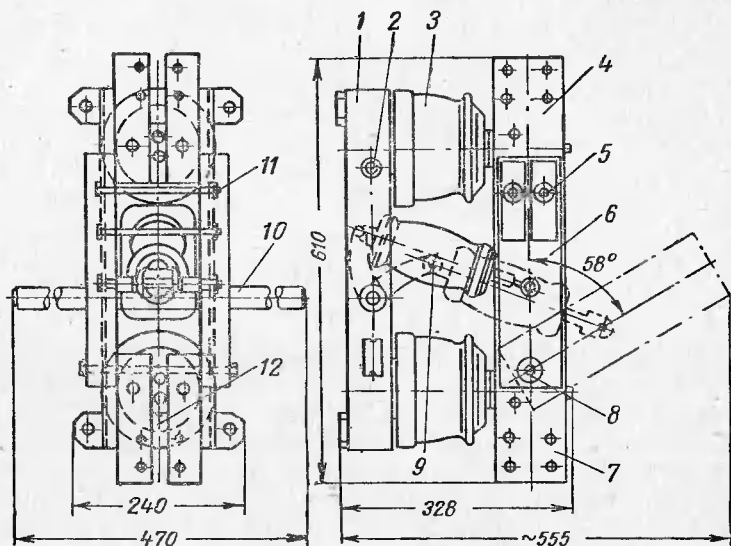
Разъединитель типа РВК-10/3000 (полюс).
